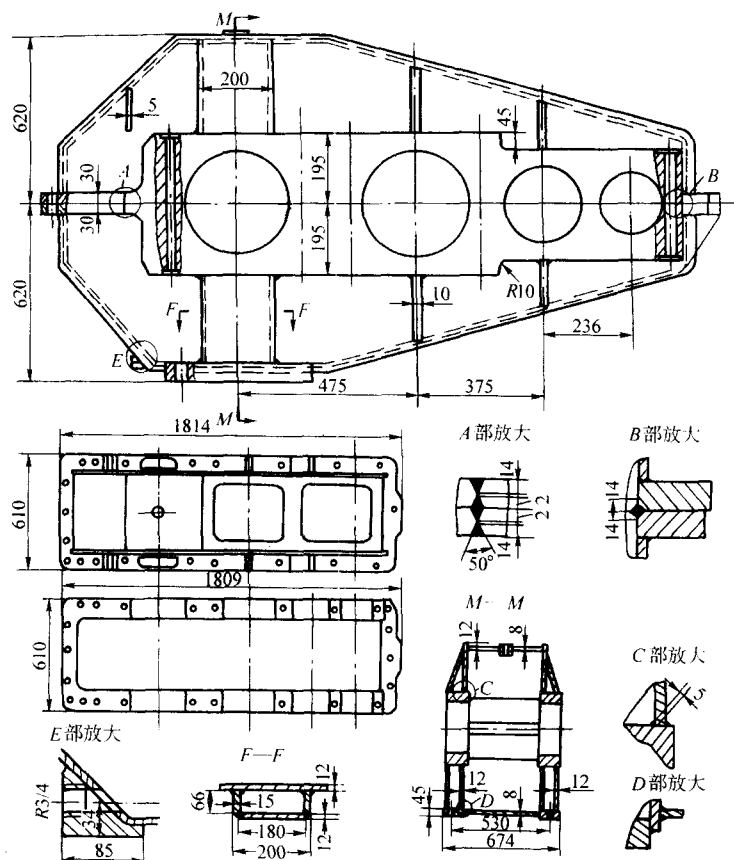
上下对称的剖分式减速器焊接箱体
